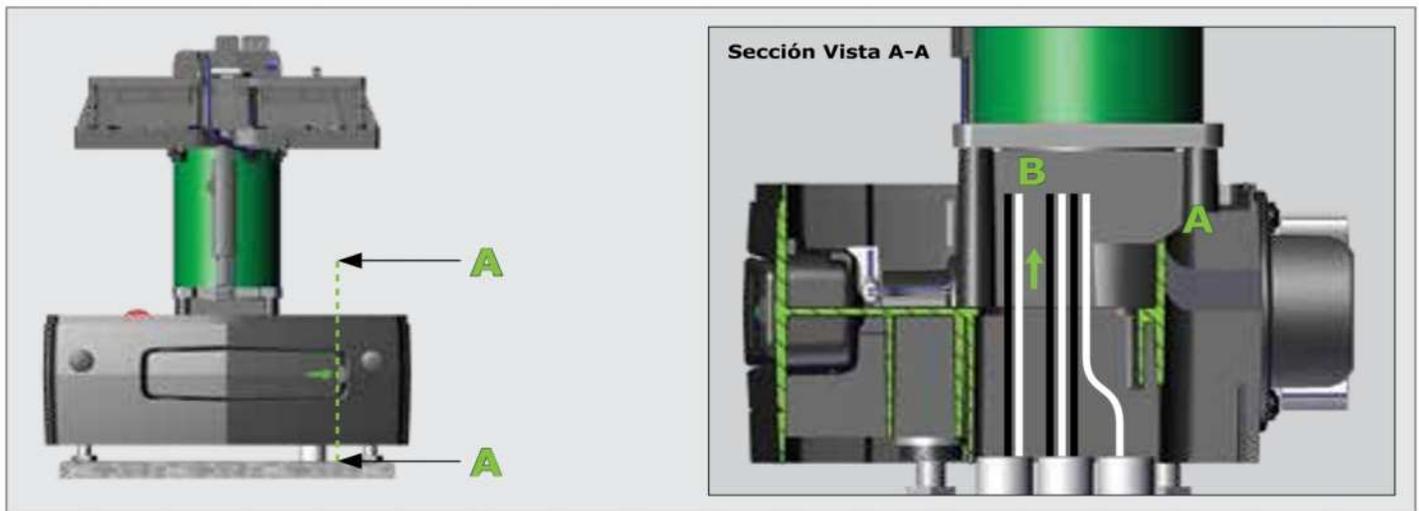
ENRUTAMIENTO DE CABLES PARA INSTALACIONES DE READAPTACIÓN DE CABLE CORTO
